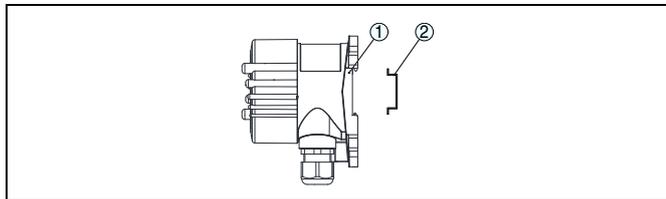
VEGADIS 81 и 82 с пластиковым корпусом для монтажа на несущей рейке
